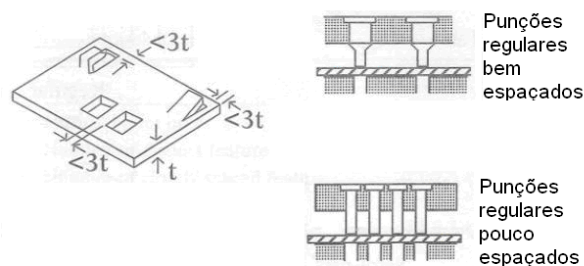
Características pouco espaçadas [Ref. 9]
